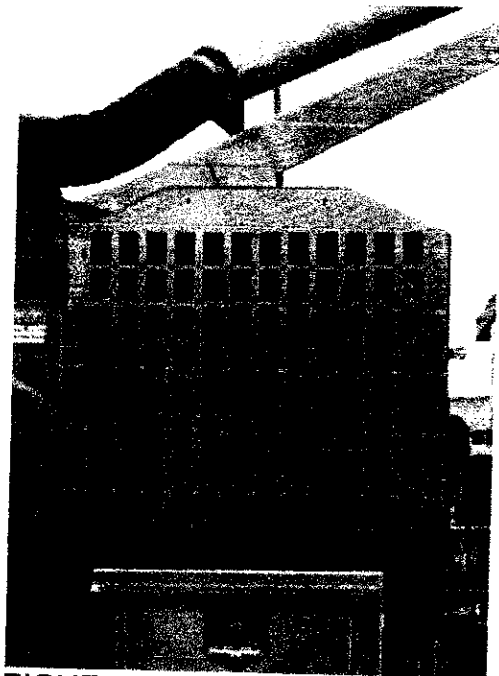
MONTAJE CAJA DE CUBIERTA MOTOR AUXILIAR
